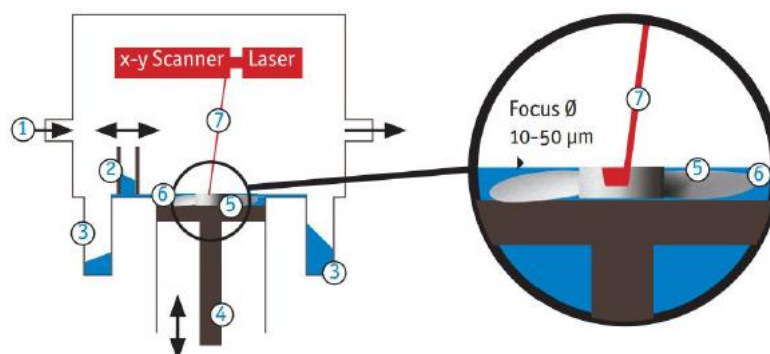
Схема СЛС-процесса. 1 – инертный газ; 2 – рапель, выравнивающий слой порошка; 3 – контейнеры с металлическим порошком; 4 – механизм управления движением платформы; 5 – строящаяся деталь; 6 – поверхность построения; 7 – сфокусированный лазерный луч [18]
